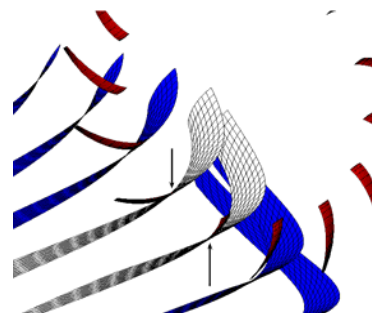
Зацепление рабочих поверхностей зубьев
